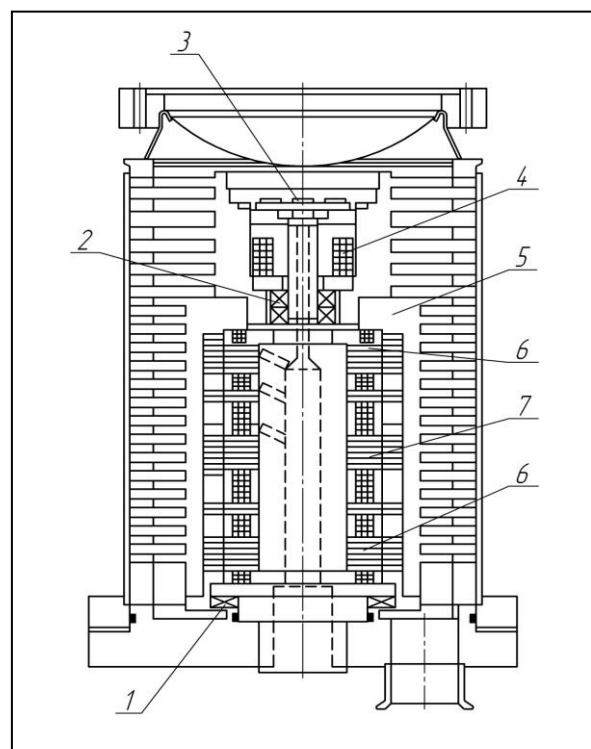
Конструктивная схема турбомолекулярного вакуумного насоса «Turbovac – 550M» с магнитной подвеской ротора: 1 – нижняя часть стержня; 2 – верхняя часть стержня; 3 – опорный стержень; 4 – осевой магнитный подшипник; 5 – полый ротор; 6 – радиальный магнитный подшипник; 7 – электродвигатель
